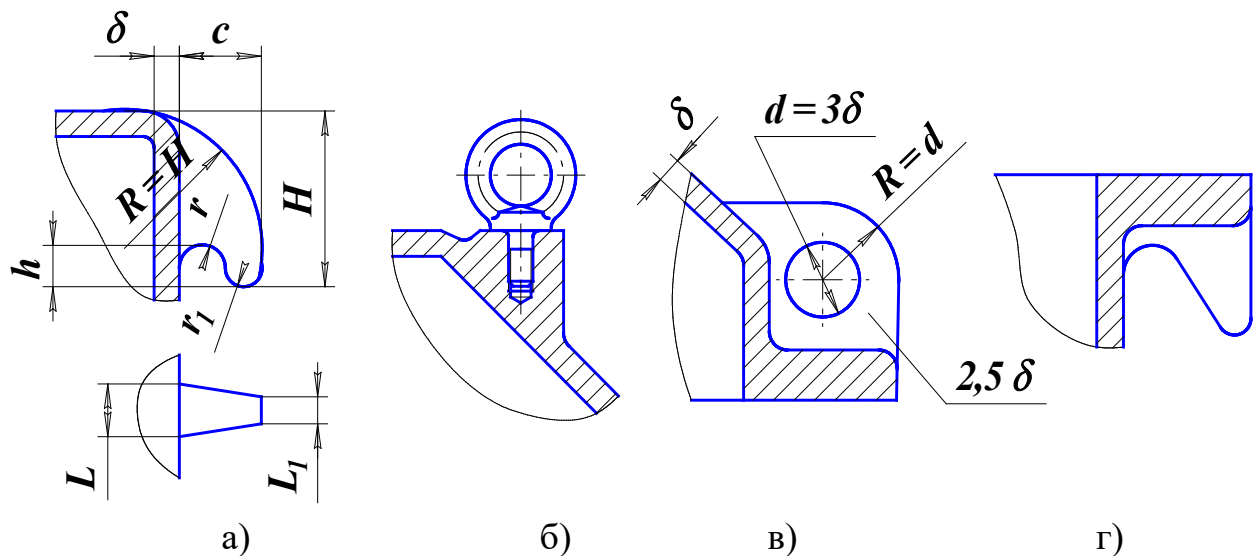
Строповочные устройства редукторов: а – прилив в корпусе, б – рым-болт, в – отверстие в ребре жесткости корпуса, г – крюк
